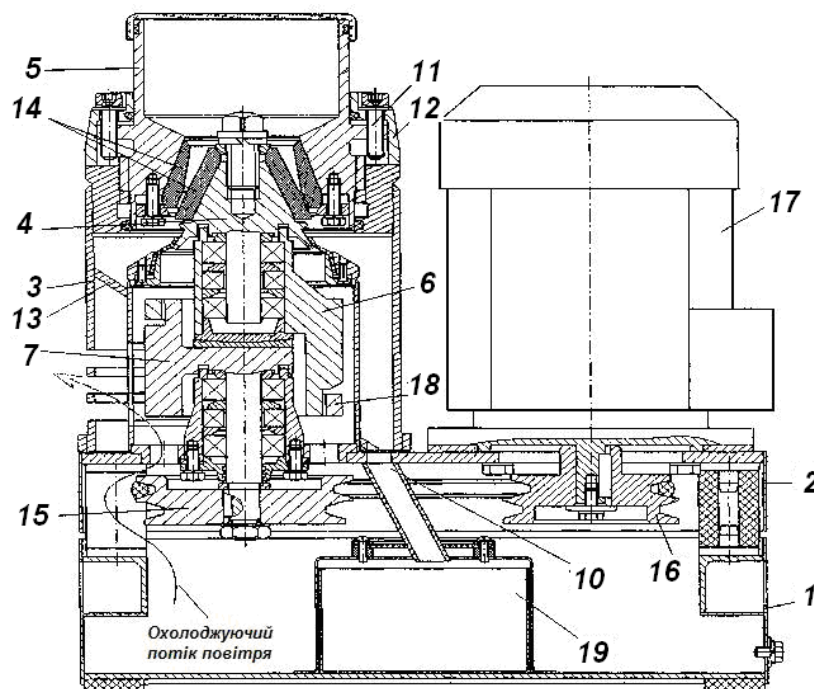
Вібраційний конусний млин-дробарка (ВКМД 6)
